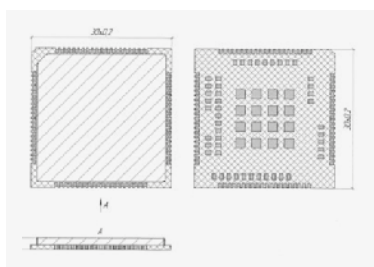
Внешний вид и размеры модуля ПР1603НБ
